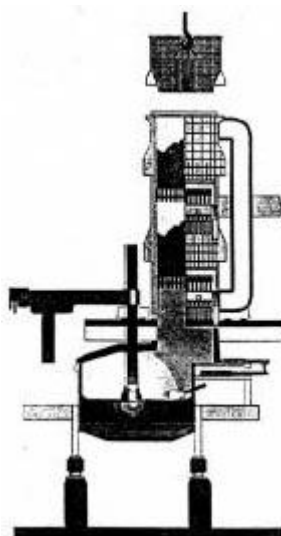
Двухкамерная шахтная дуговая печь с удерживающими пальцами
